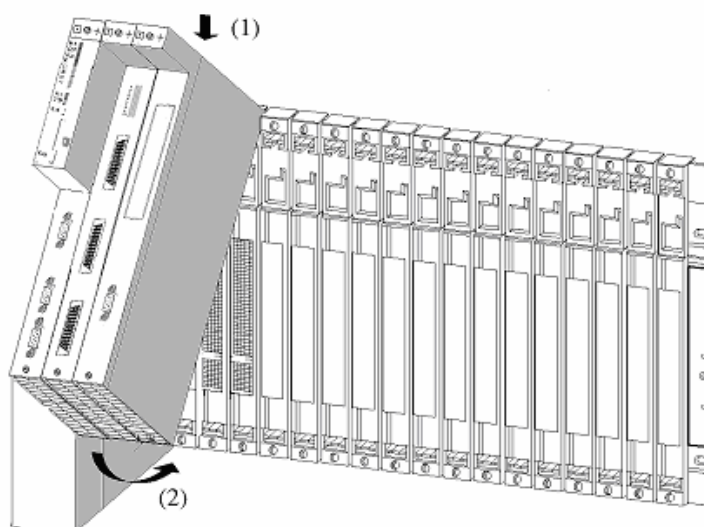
Baugruppe FM 458-1 DP einhängen (Prinzipbild)
